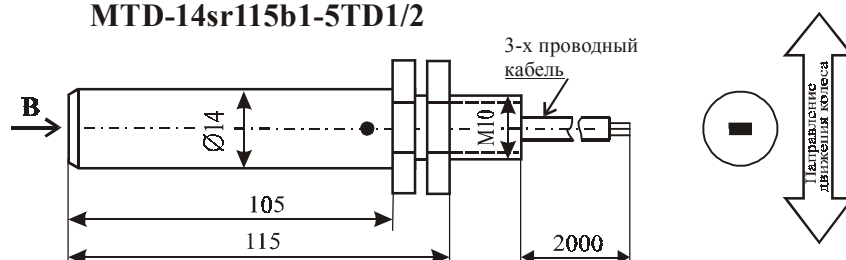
Внешний вид и габаритные размеры датчиков типа MTD-14er115b1-5TD1/2
